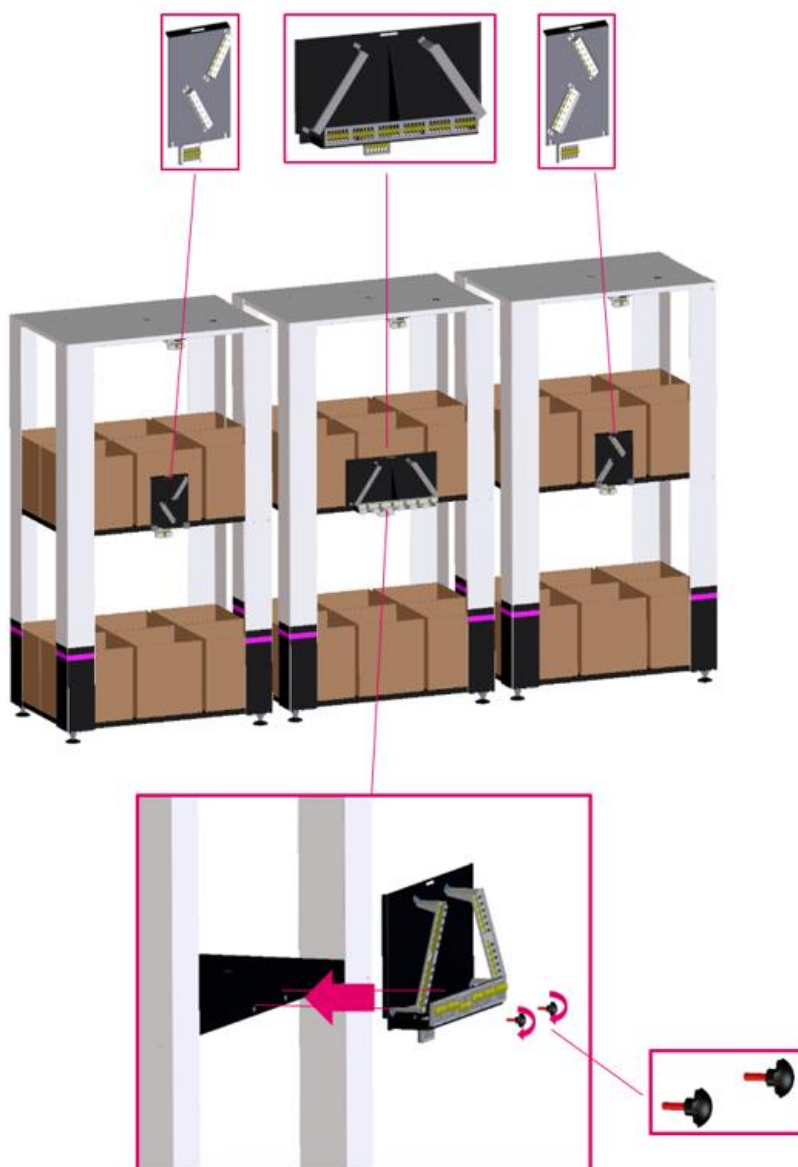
Montaje de las piezas de desvío en el organizador de cables
